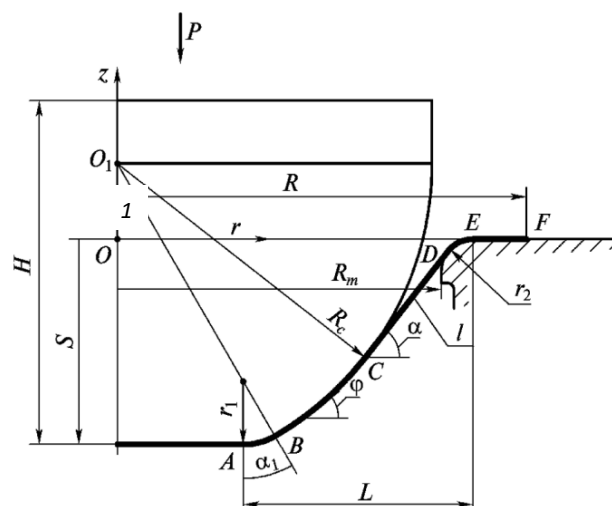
Расчетная схема глубокой вытяжки сферической детали
